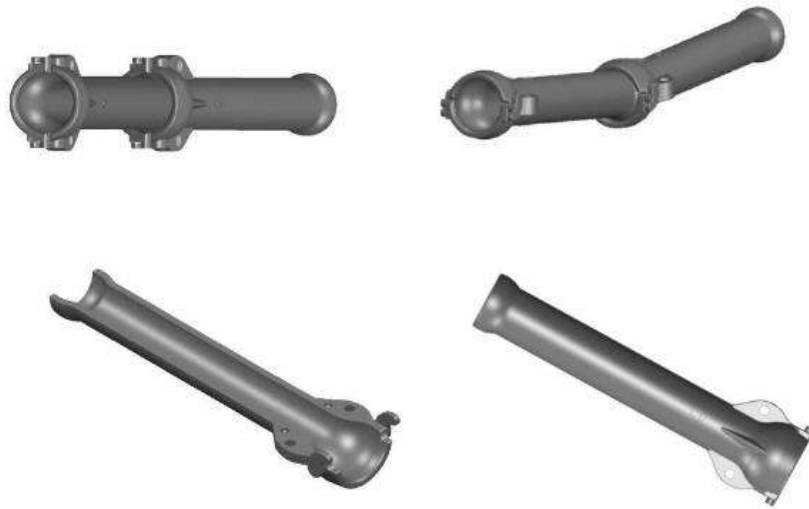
Ejemplo de tuberías articuladas para proteger el cable en la zona de aterrizaje. Fuente: NEC.
